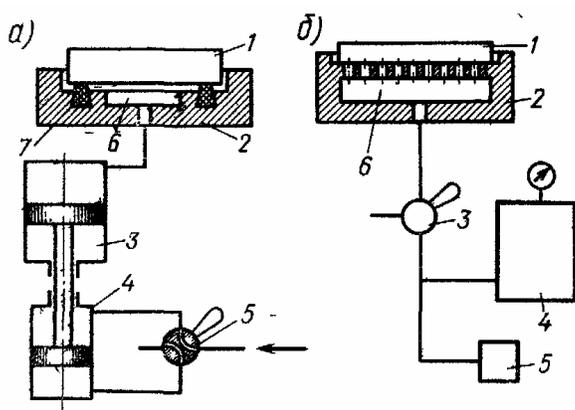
Схемы приспособлений с вакуумным приводом (а – с применением пневмоцилиндра; б – применением вакуумного насоса)
